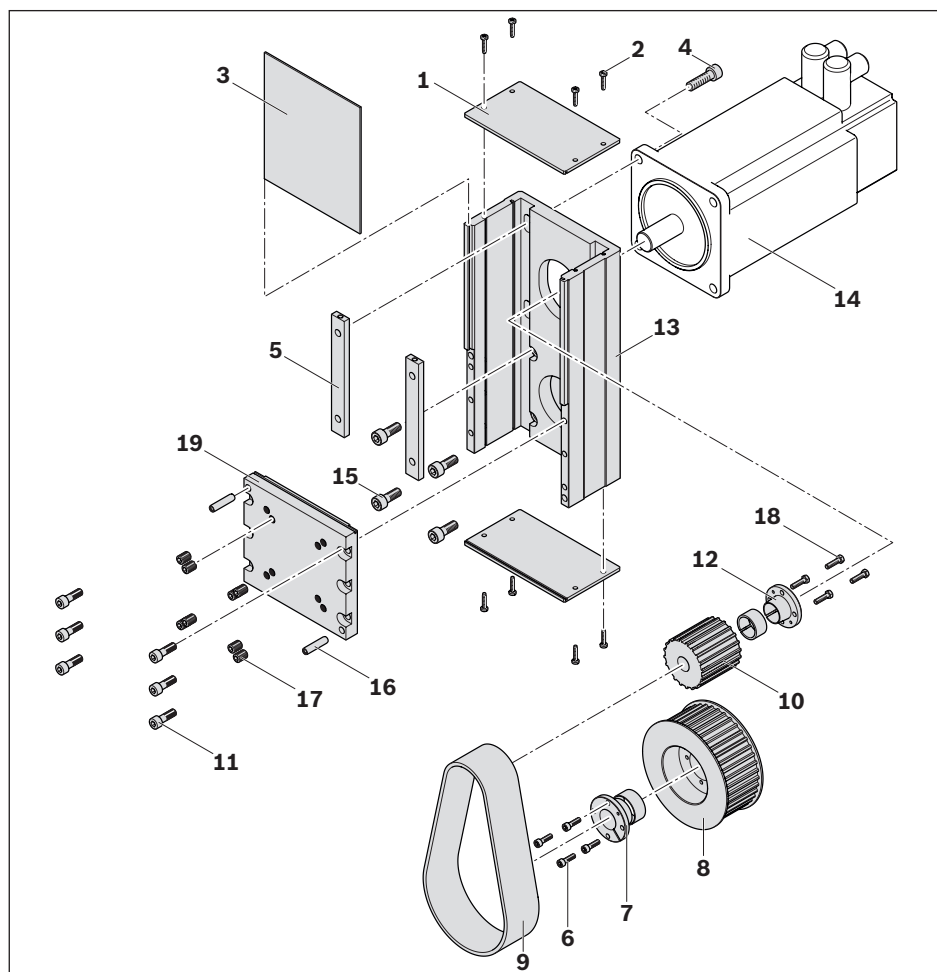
Montaje del motor con transmisión por correa dentada sin contra-apoyo
